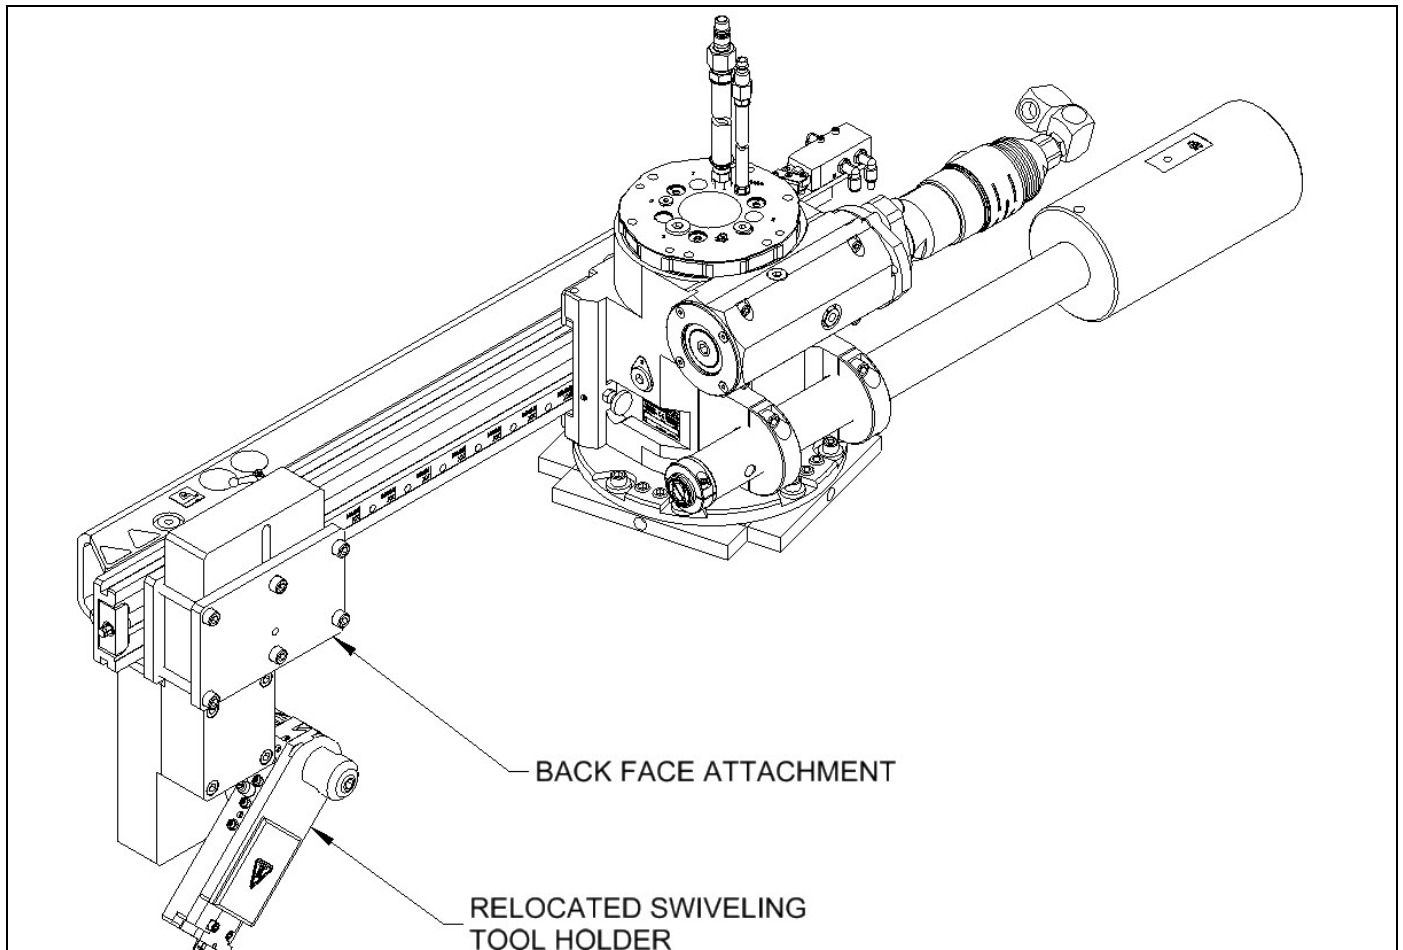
FF6300 FIXATION EN FACE ARRIÈRE SUR LA MACHINE MONTÉE EN FACE AVANT
